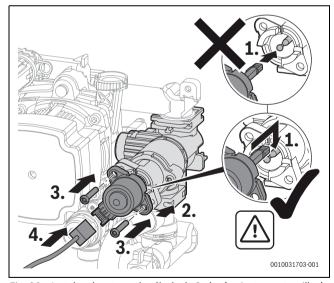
Instalar el motor en la válvula de 3 vías (variante con tornillos)
